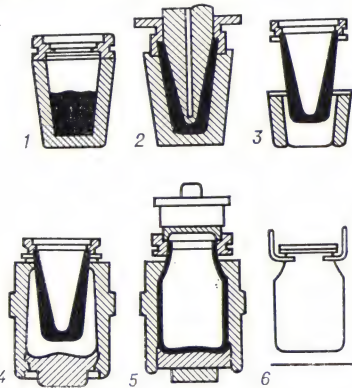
Схема выработки изделий на прессовывудной машине: 1 — приём капли; 2 — выпрессовывание пульки в черновой форме; 3, 4 — передача пульки из черновой формы в чистовую; 5 — выдувание изделия в чистой форме; 6 — отставление готового изделия на конвейер.
